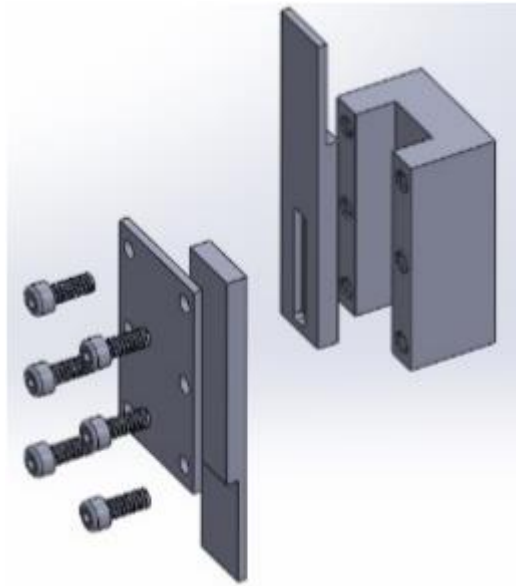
Vista explodida do modelo CAD do dispositivo da patente o nº BR 10 2016 021054 2.
